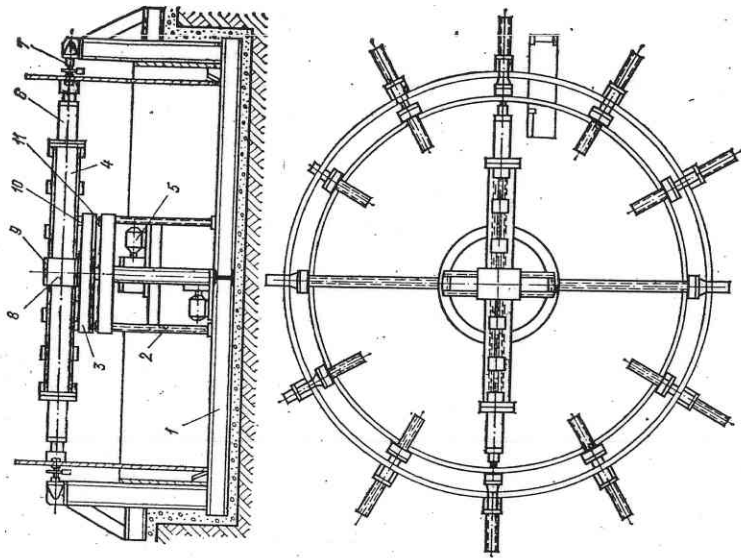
Распорное устройство (симметричное) для сборки обечаек в звено:
